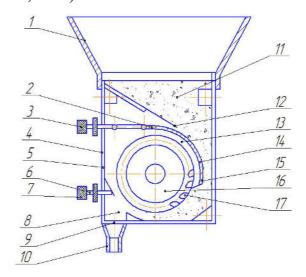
Схема порошкового питателя (АС СССР №54731,
